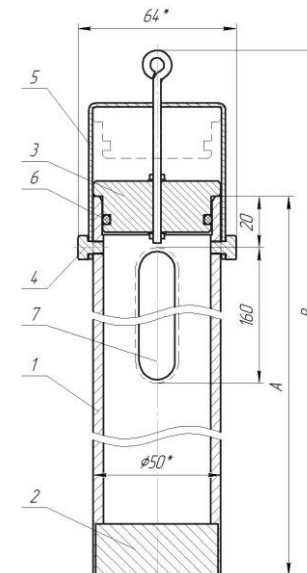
Эскиз пробоотборника типа ПДА. 1 – корпус; 2 – дно; 3 – крышка; 4 – винты; 5 – поворотная рамка; 6 – уплотнительное кольцо; 7 – смотровое окно.
